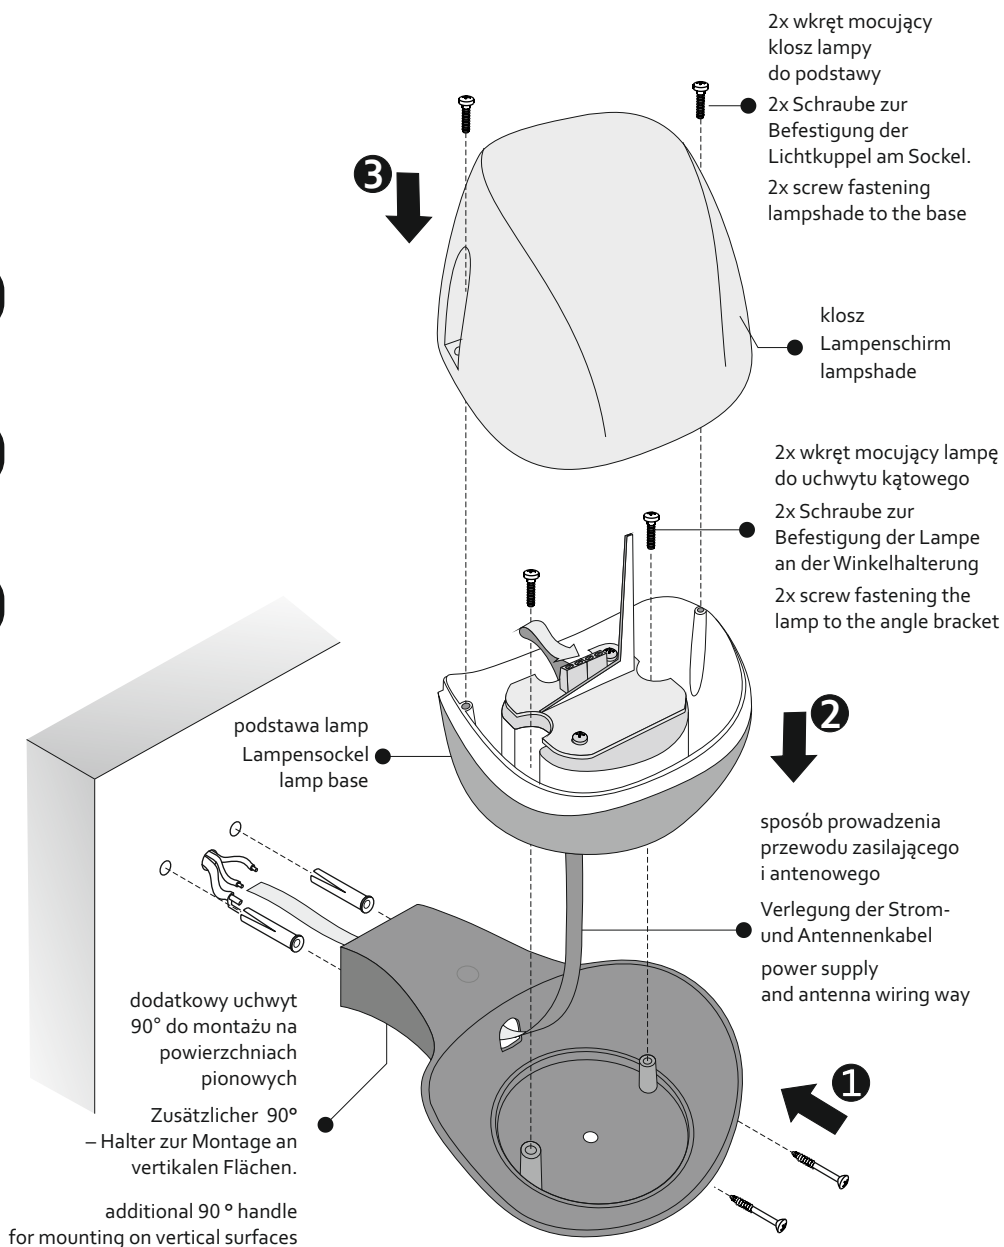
Montage der Lampe auf einer horizontalen Fläche.
